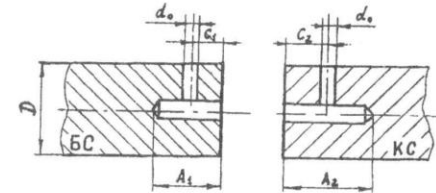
Заготовки под сварку инструмента с уменьшенной площадью свариваемого сечения
